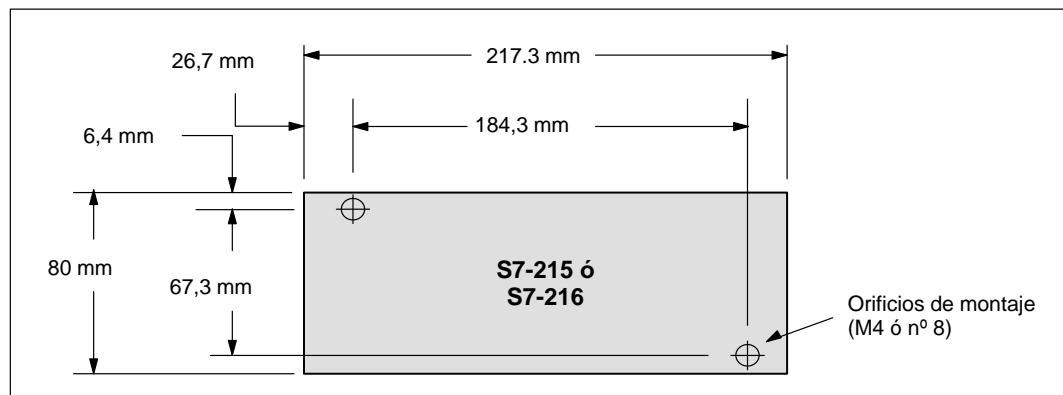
Dimensiones de montaje para una CPU S7-215 ó S7-216
